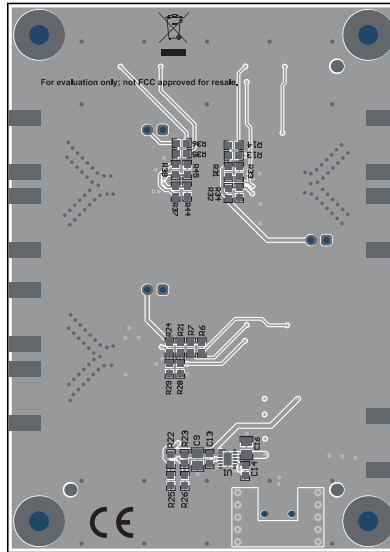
LMK6BEVM の PCB レイアウト例 - 最下層
